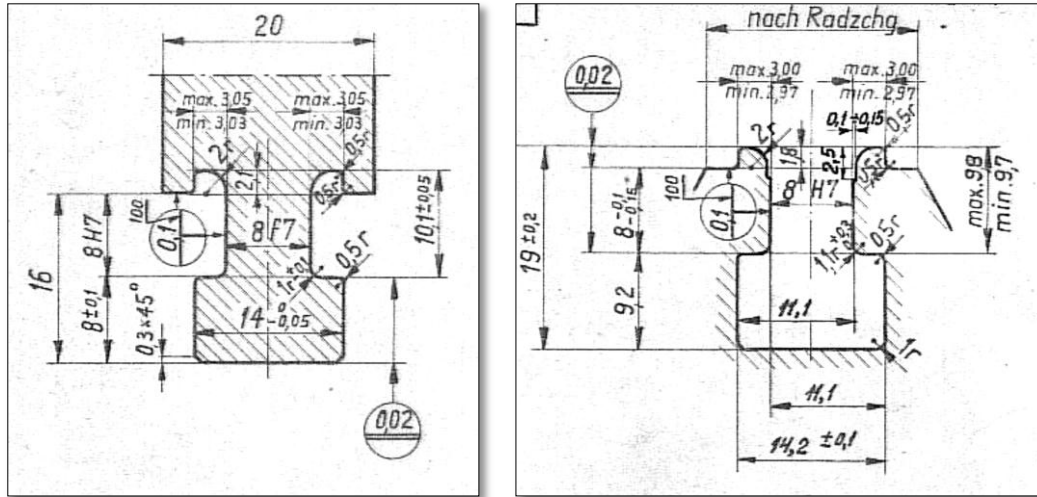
dimensioni del piede palare (a sinistra) e della cava (a destra) sul disco del 9° stadio della macchina n° 1.
